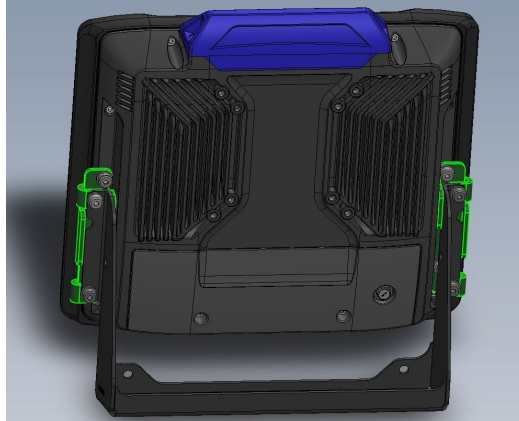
Montagebügel mit Adapter am DLT-V73
